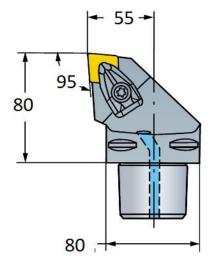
Резец проходной C8-DCLNL-55080-16
